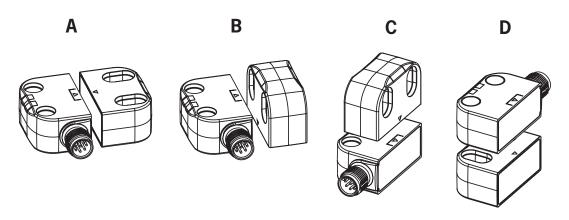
Posizioni di installazione ammesse con l'azionatore CES-A-BTN-C07-...: rispettare la direzione della freccia sul dispositivo.
